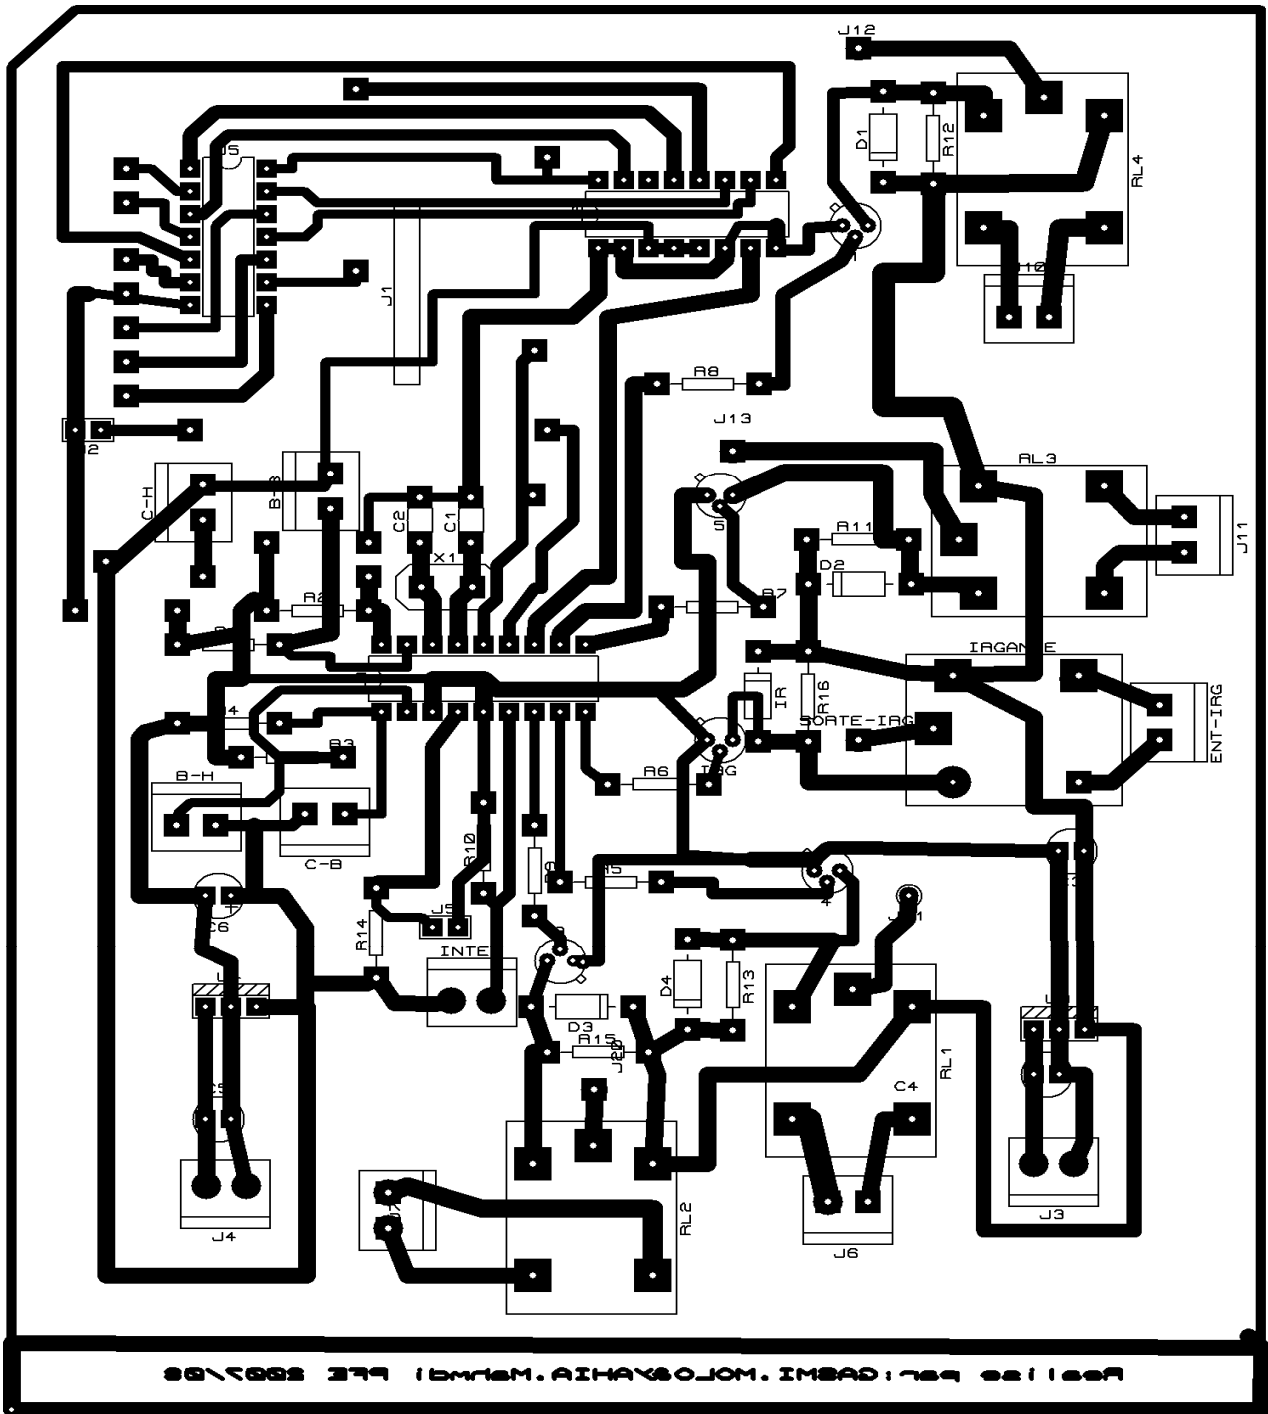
Circuit imprimé (face soudure).
